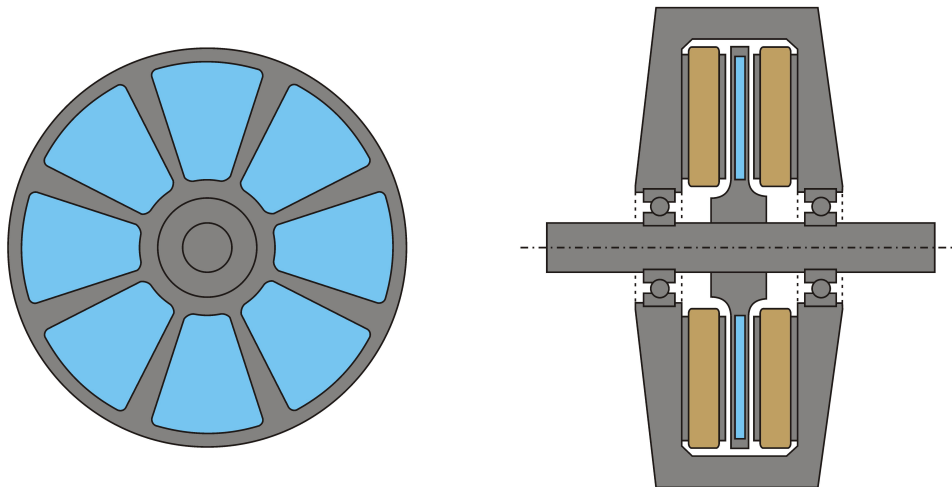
Seitenansicht der Welle und Schnittbild der gesamten Axialflussmaschine mit beidseitigem Stator nach Knörzer und von König (2000)
